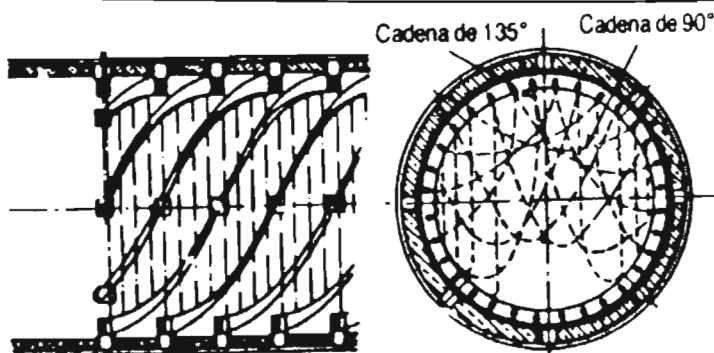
Instalación de cadenas de horno. (Fuente: Ref. 10)
